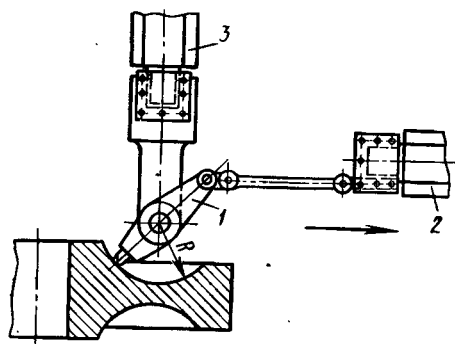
Приспособление для обработки криволинейных поверхностей:
